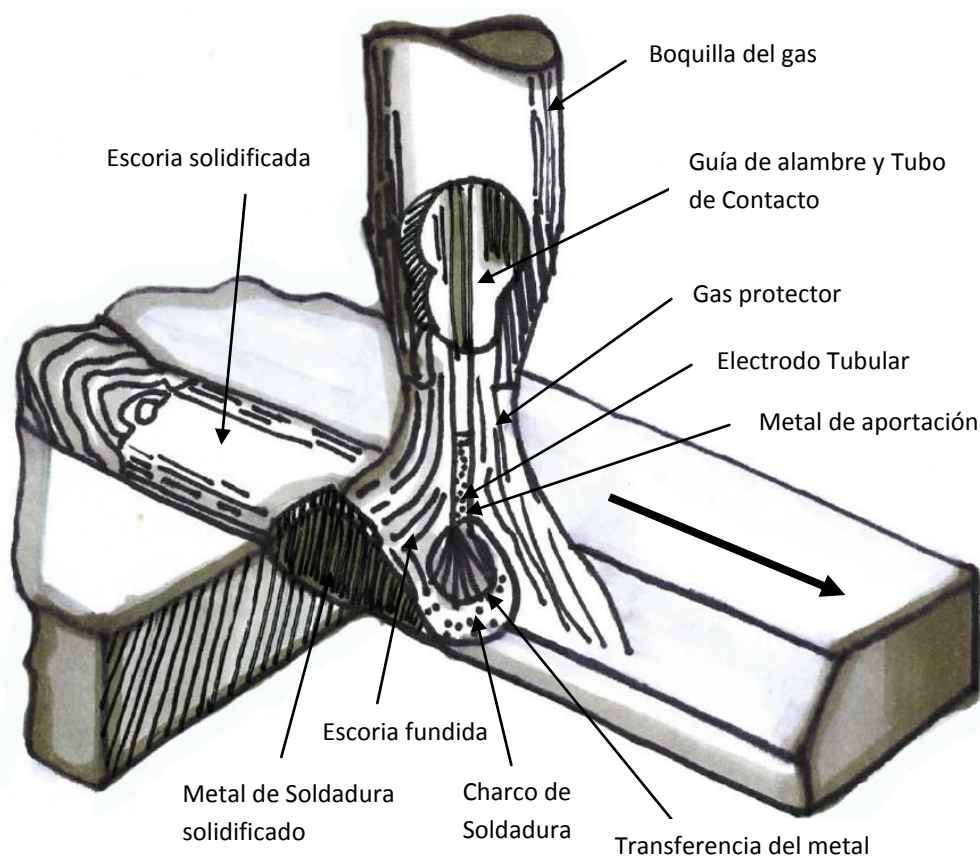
Aplicación de soldadura de ranura
